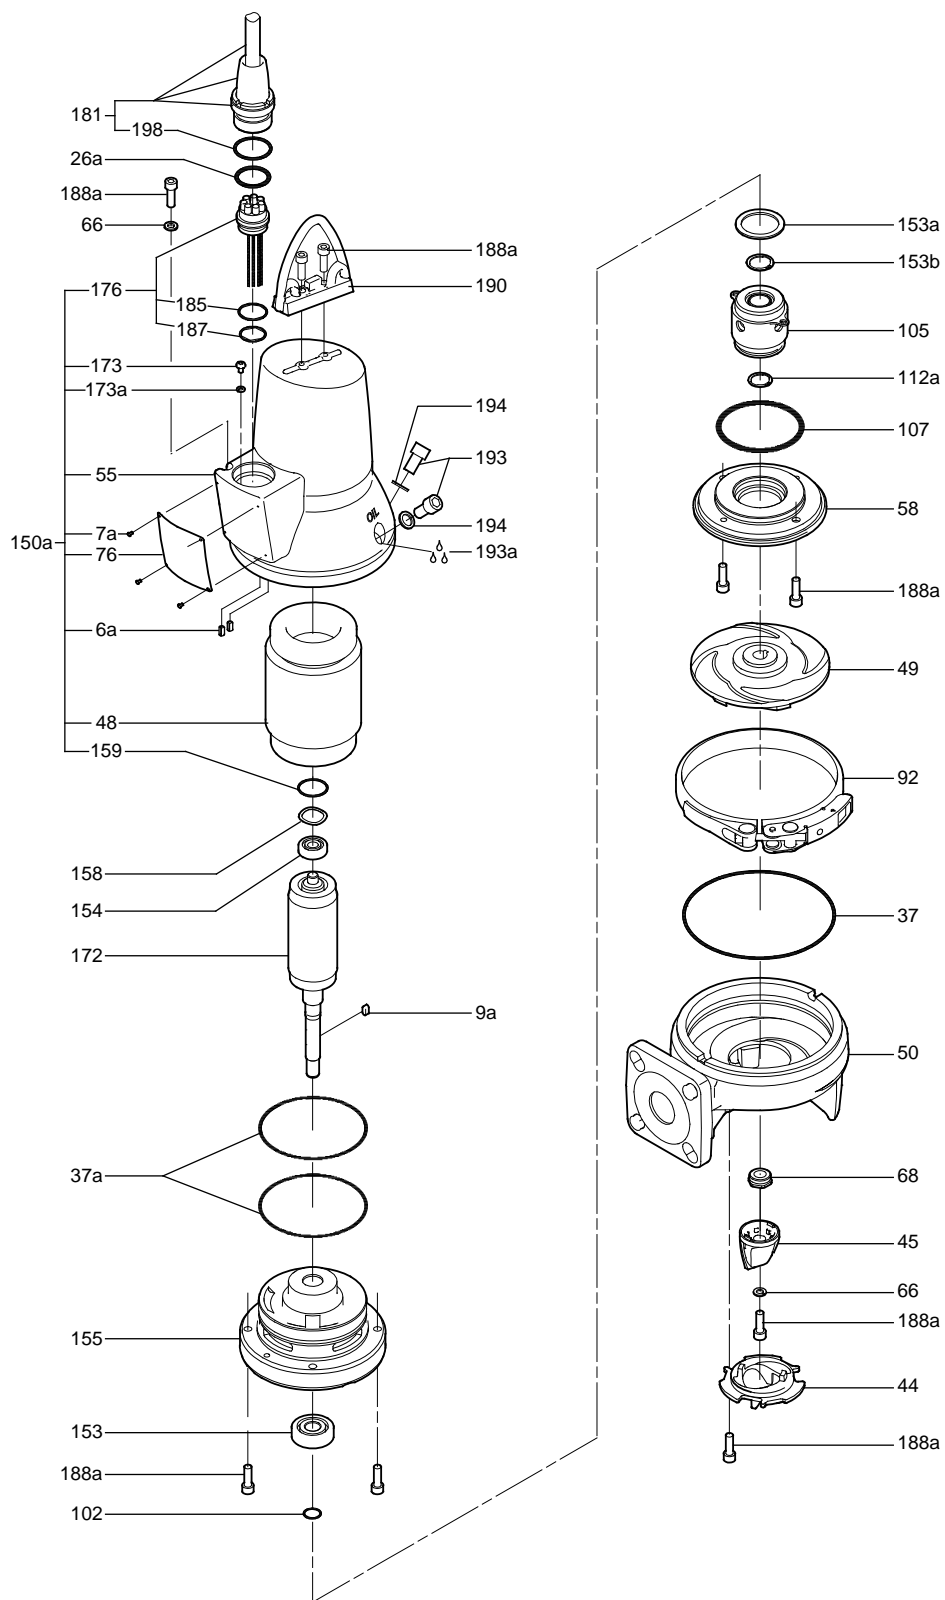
Vue éclatée des pompes SEG, 2,6, 3,1 et 4,0 kW
